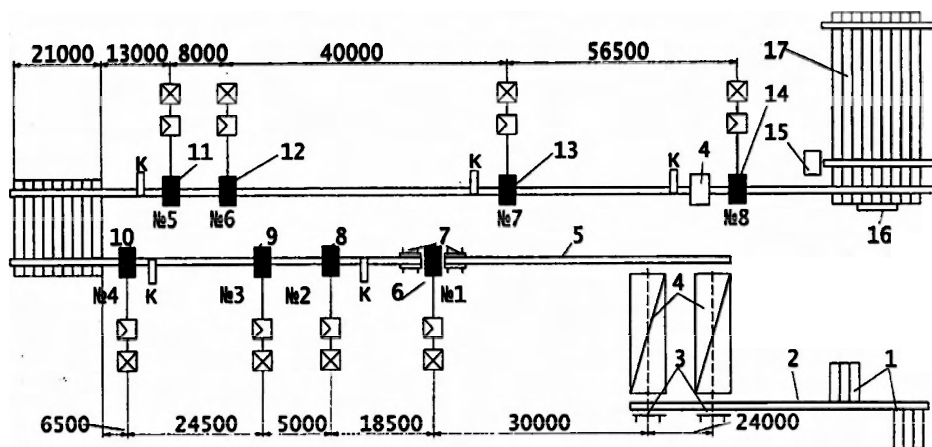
Схема расположения основного технологического оборудования участка печей и непосредственно стана 550-2: 1 - загрузочные устройства; 2 - загрузочный рольганг; 3 - сталкиватели; 4 - нагрева тельные печи; 5 - приемный рольганг; 6 - обжимная реверсивная клеть дуо; 7 - кантователи-манипуляторы; 8-13 - рабочие неререверсивные клетки дуо с предварительно напряженными станинами; 14 - рабочая неререверсивная клеть дуо периодической прокатки; 15 - пила горячей резки для отбора проб; 16 - переключивающее устройство; 17 - холодильник; К - кантующие валки.
